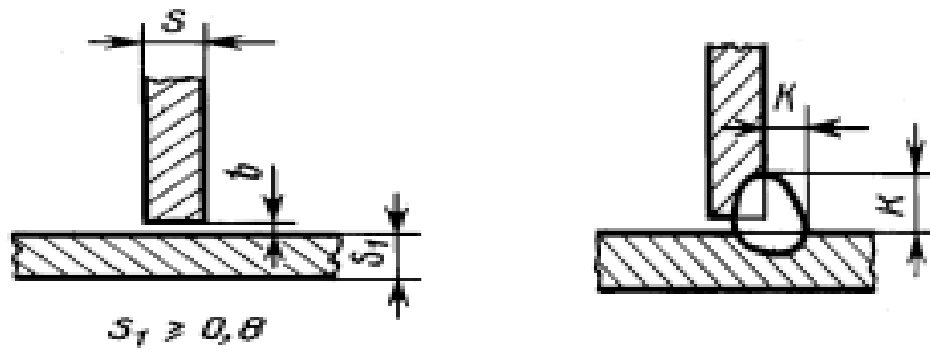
Конструктивні елементи підготовки кромки, що зварюються: S , S_1 – товщина деталі; b – зазор
